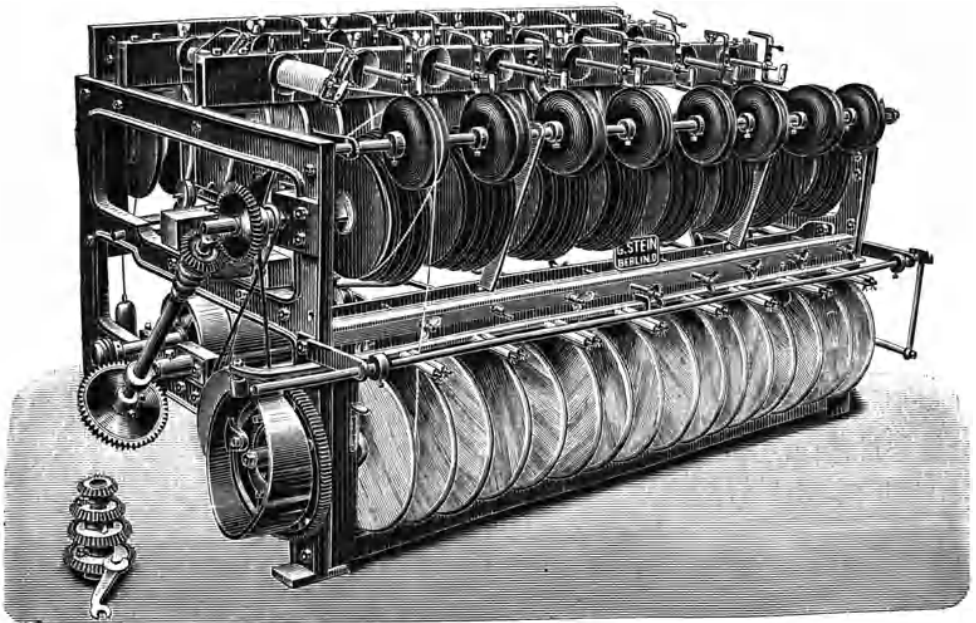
Umspinnmaschine von G. Stein zur gleichseitigen Bessinnung von acht dünneren Drähten.
